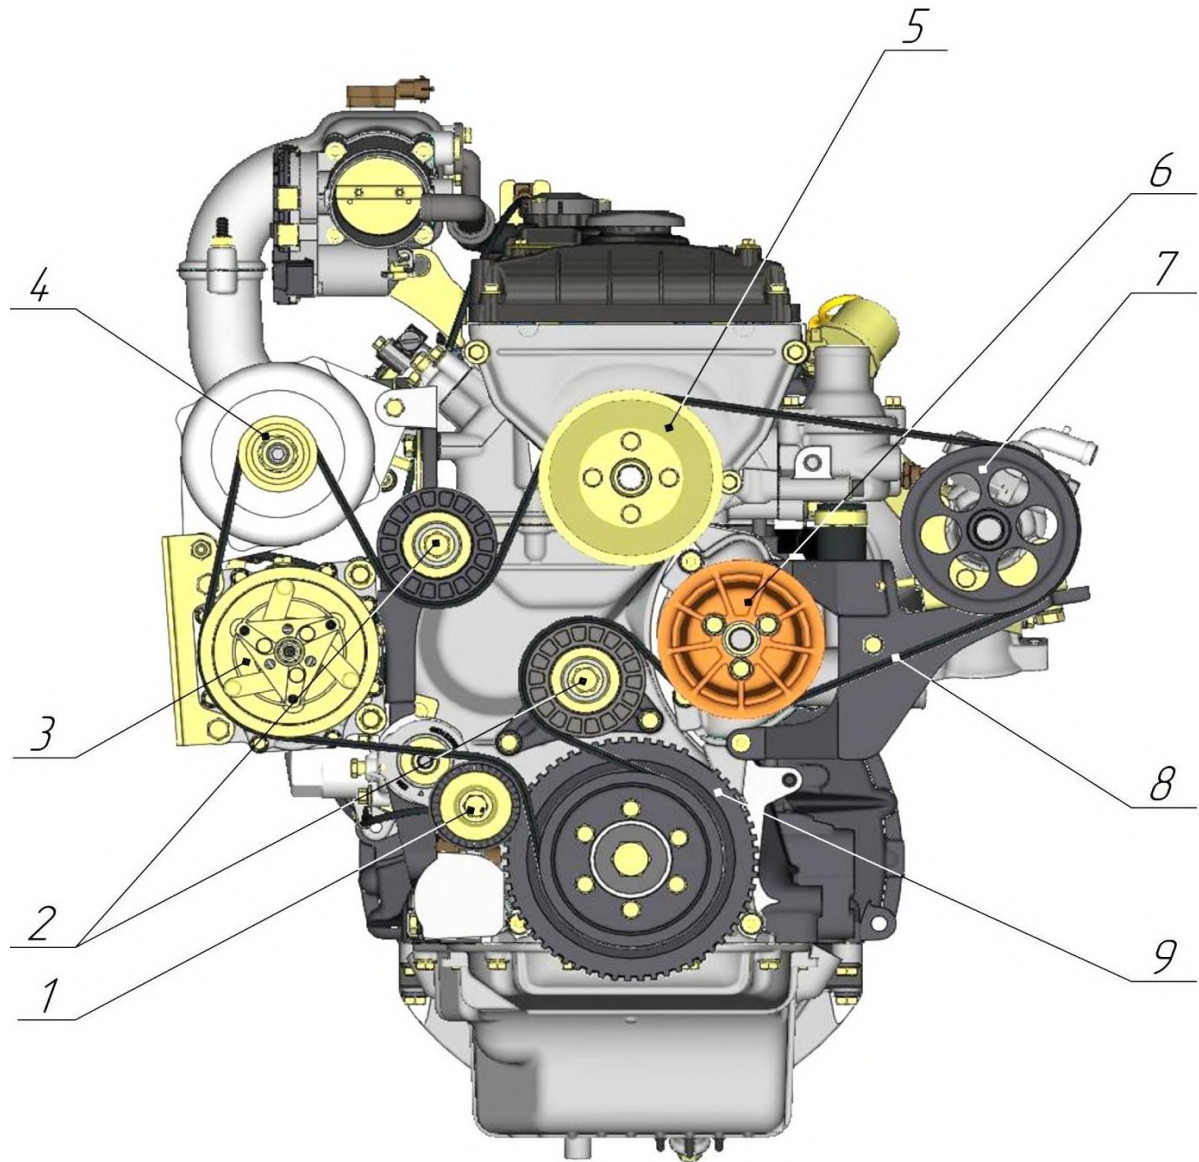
Vorderansicht des Motors ZMZ-40905.10 mit Klimakompressor und Servolenkungspumpe:
